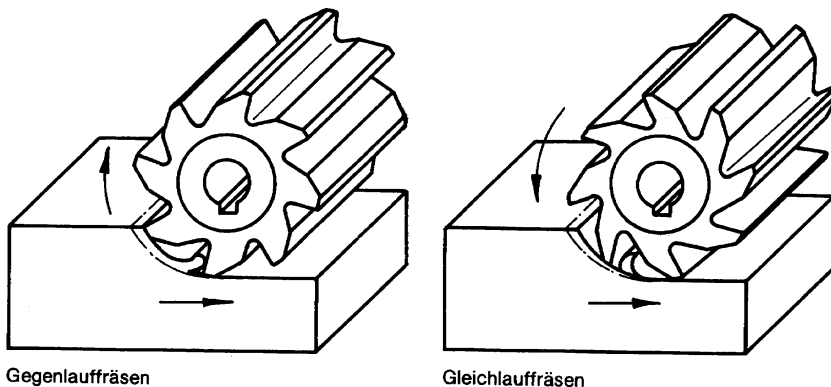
Umfangsplanfräsen - Gegenlaufplanfräse/Gleichlaufplanfräse
